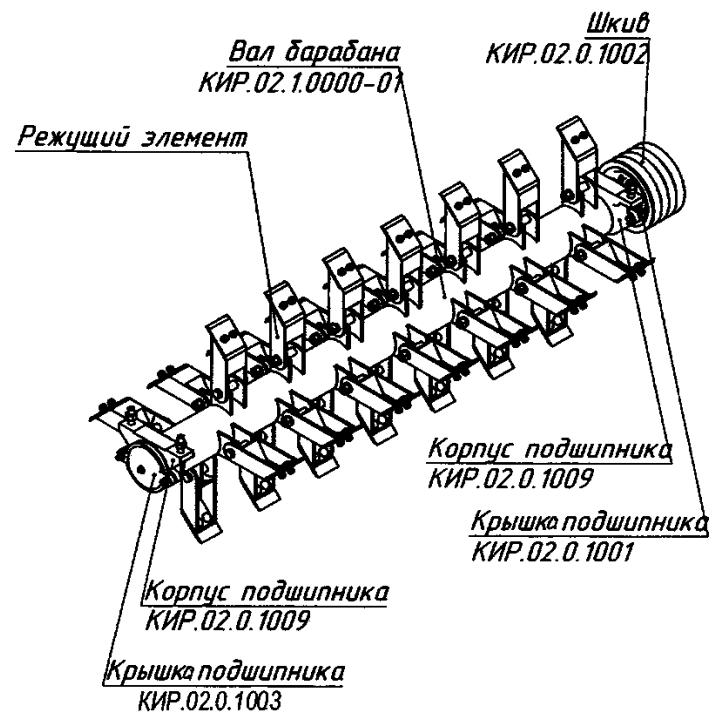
Барабан модернизированный КИР.02.0.0000-01
